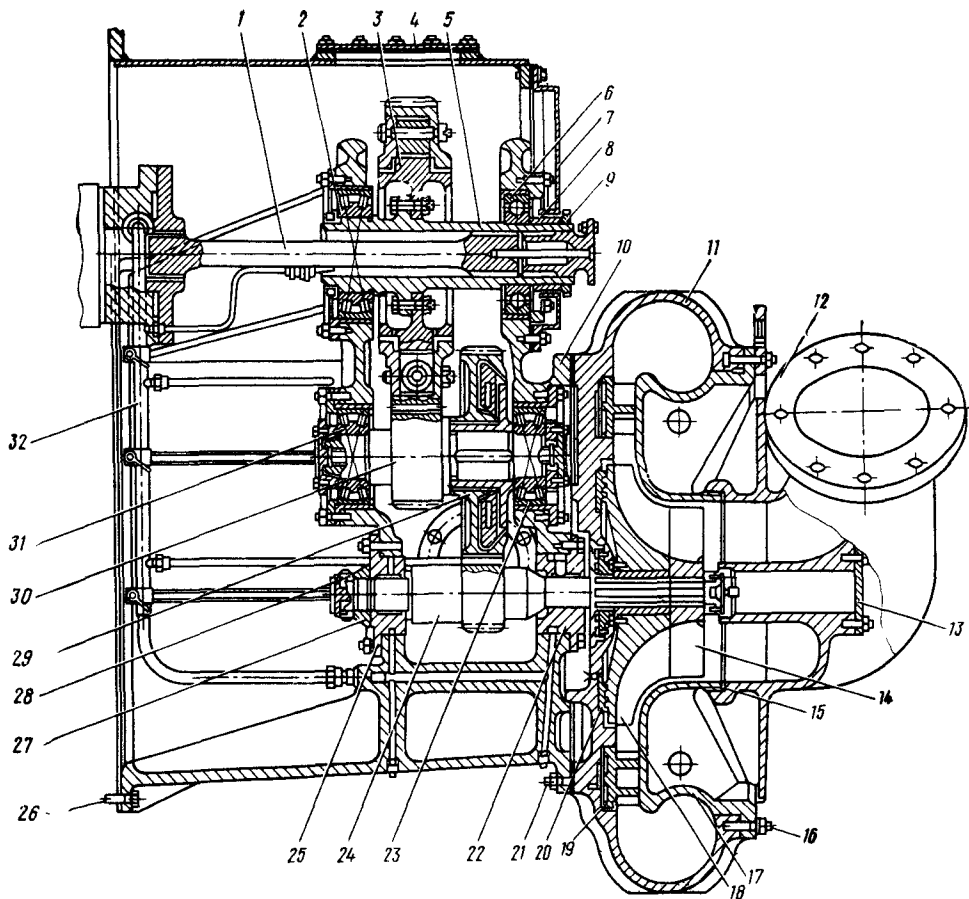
Центробежный нагнетатель второй ступени с редуктором дизеля 10Д100:
